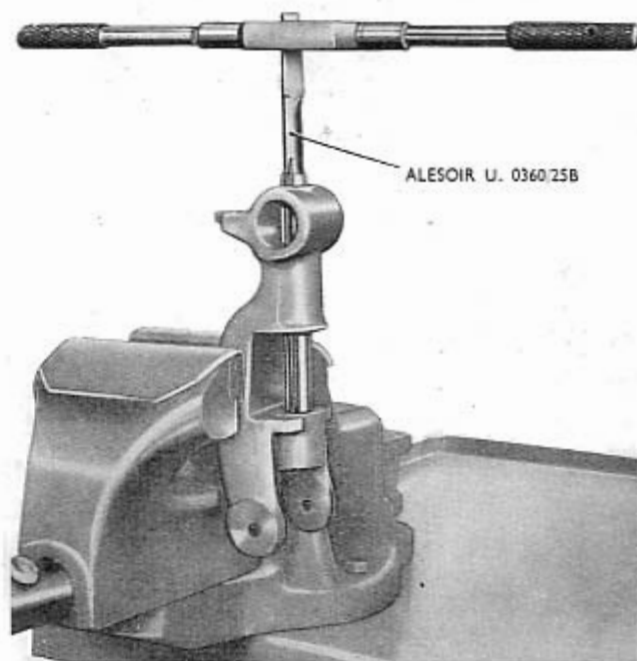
Alésage des bagues, sur le montant, du pivot de fusée, au moyen de l'alésoir U. 0360/25 B.
